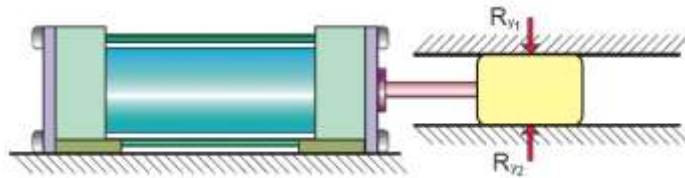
La carga avanza conducida entre superficies rígidas que anulan la acción de una fuerza lateral sobre el actuador.
